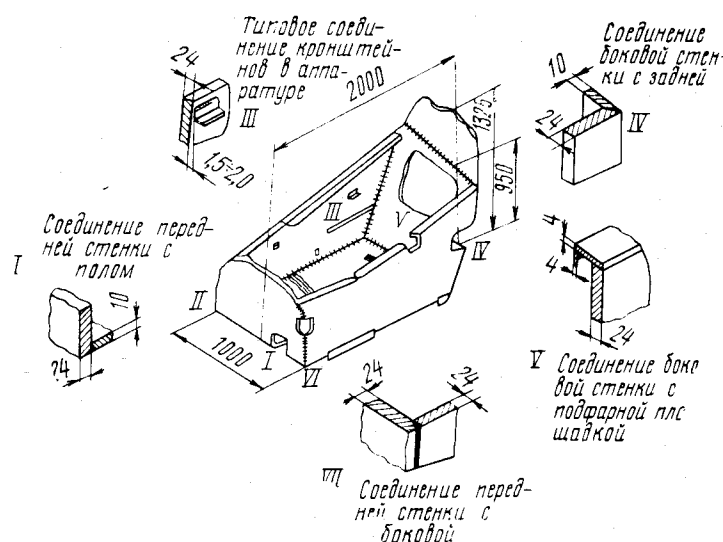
Сварной агрегат из титанового листа.
